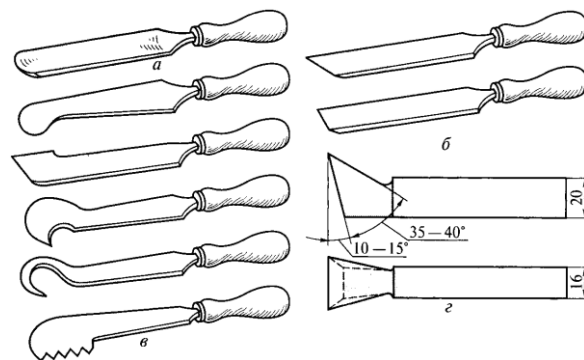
Токарні різці: *а* - з напівкруглим лезом для чорнового гостріння; *б* - із прямим лезом для чистового гостріння; *в* - фасонні; *г* - верстатний прохідний
